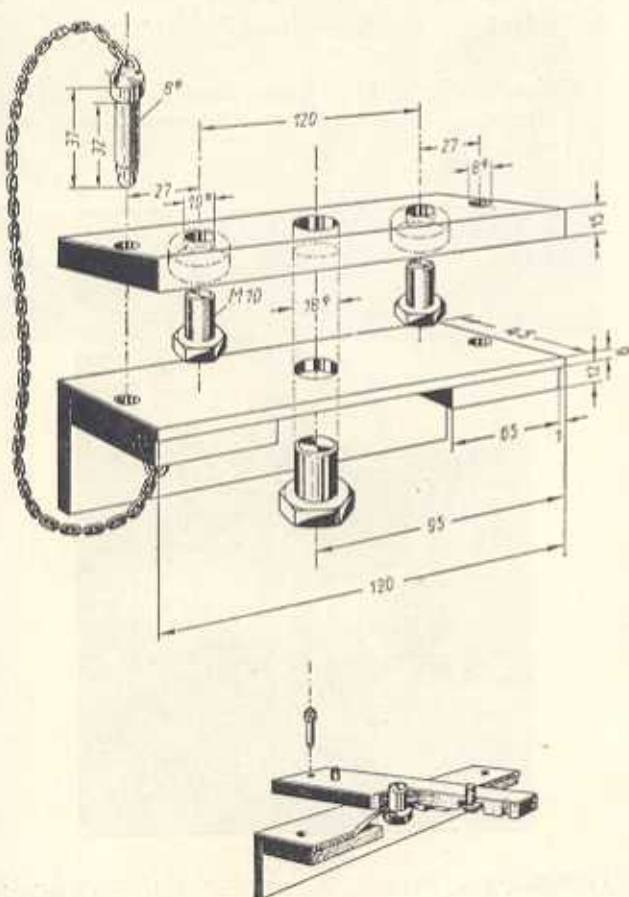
Maßskizze der Haltevorrichtung für Getriebe
